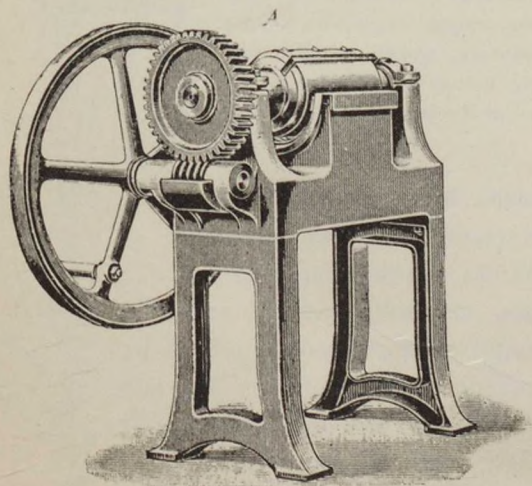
Станокъ для обстрагиванія затылка стереотипа.
